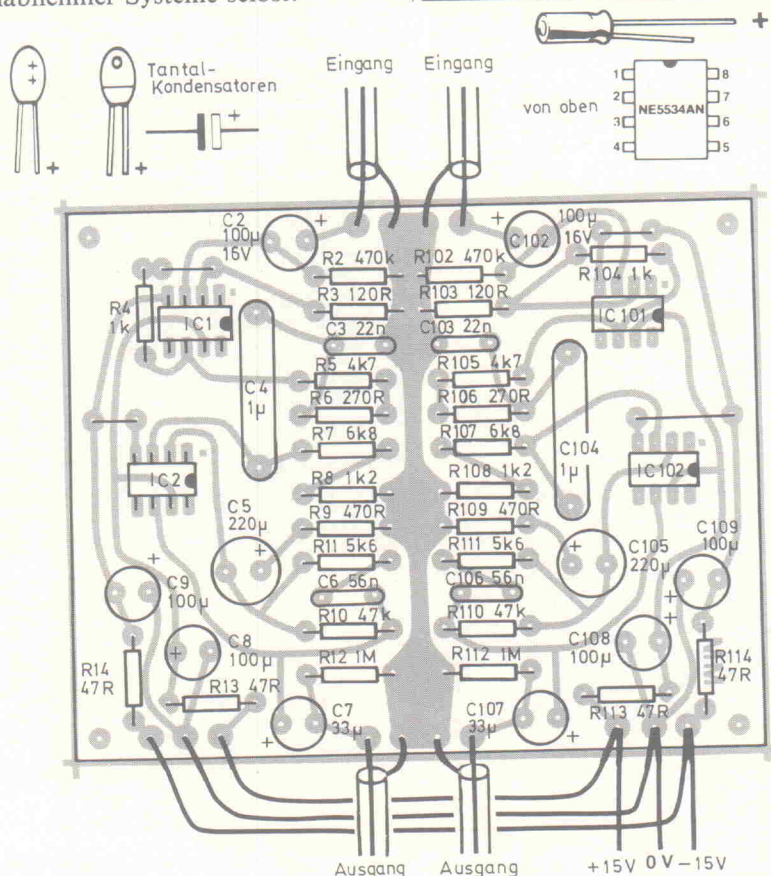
Bestückungsplan für die Moving-Magnet-Stufe (siehe auch Seite 35 für Aufbauhinweise)
